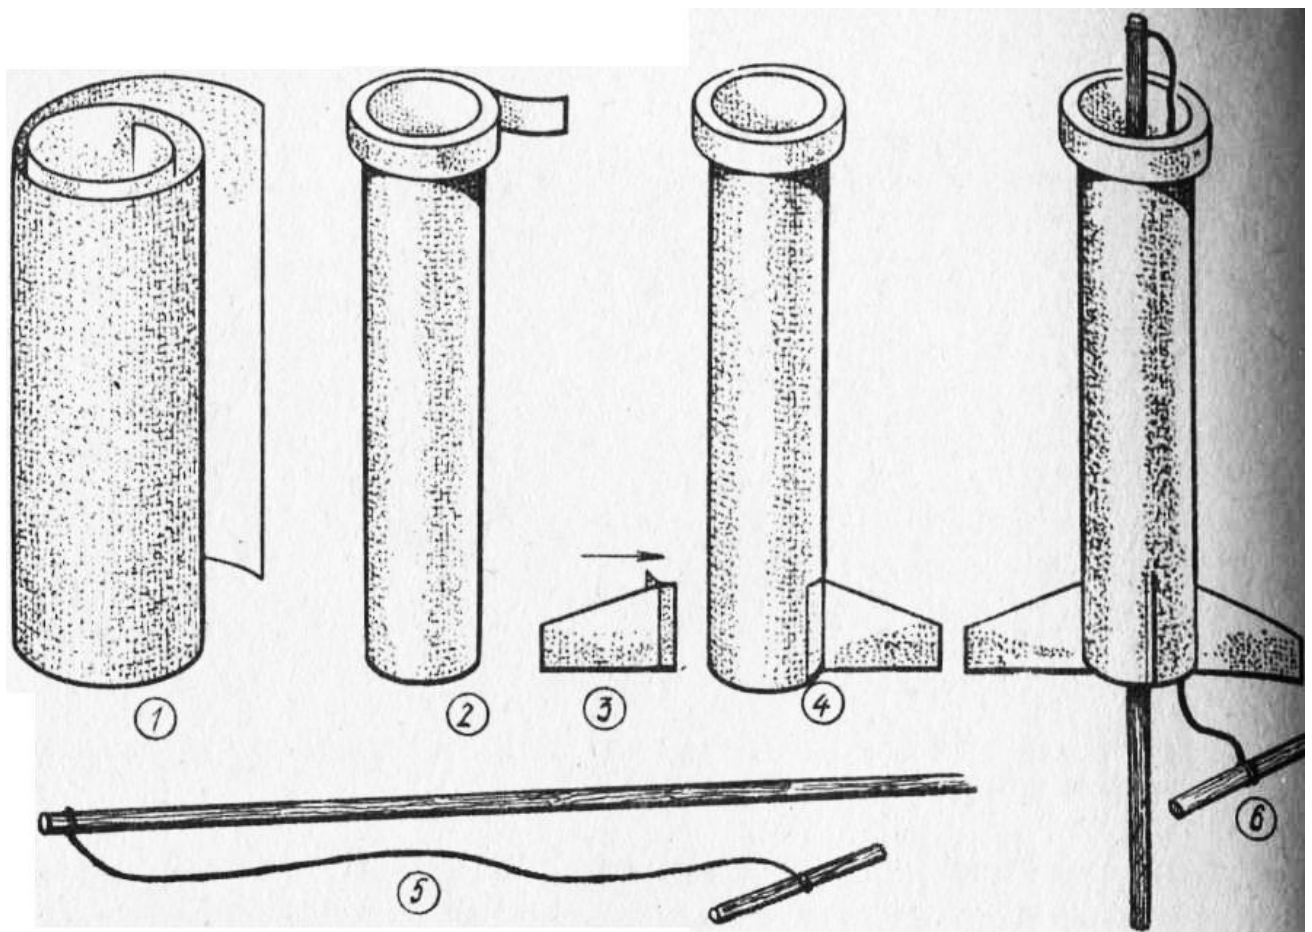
Модель летающей ракеты с пусковой установкой: 1 — изготовление бумажного корпуса ракеты (бумажная трубка); 2 — приклеивание цветной полоски бумаги к верхней части корпуса; 3 — стабилизатор; 4 — приклеивание стабилизаторов к корпусу; 5 — пусковая установка (катапульта); 6 — наглядное изображение ракеты с катаapultой
